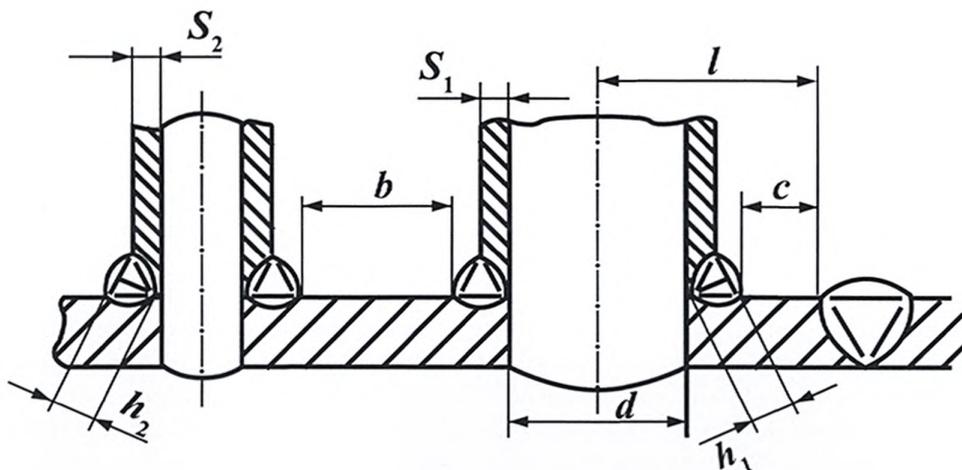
Расположение сварных соединений приварки патрубков:
